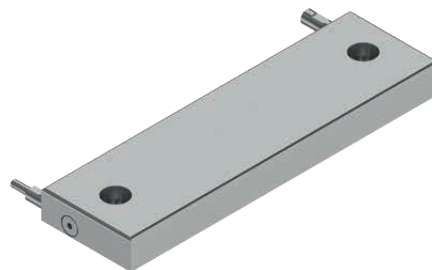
Endblock LMFC4-R-C zur Rückführung des Kühlmittels am Ende der Statoren-Bahn
